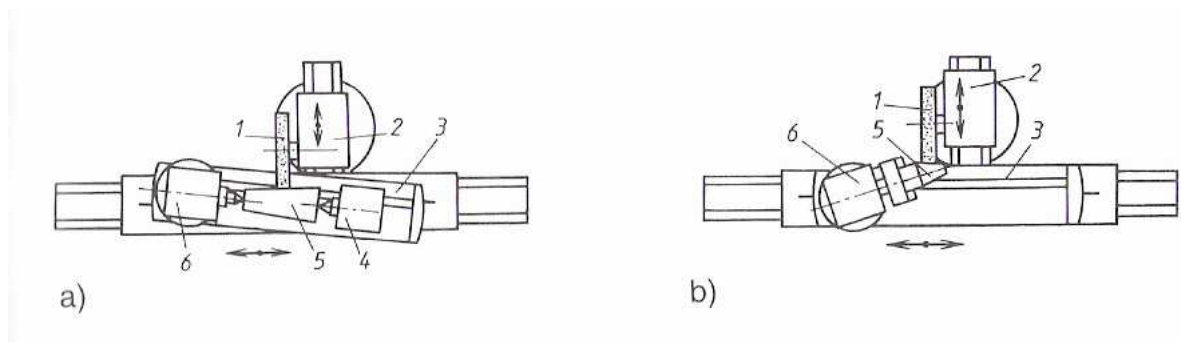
Hrotové brusky a) s posuvným stolem b) s posuvným vřeteníkem
